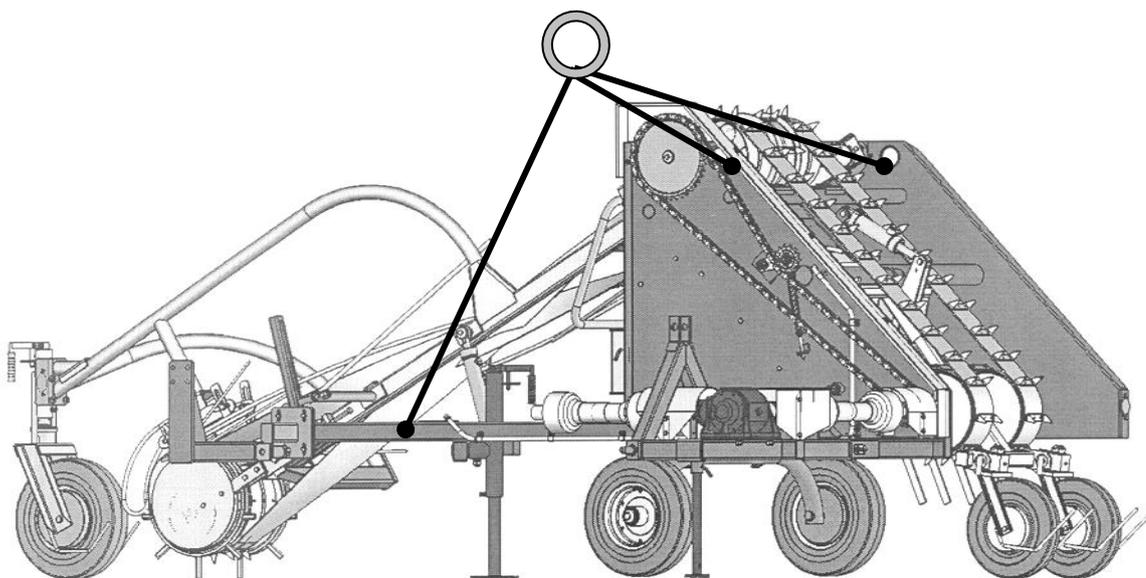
Схема строповки оборащивателя для выполнения погрузочно-разгрузочных работ
